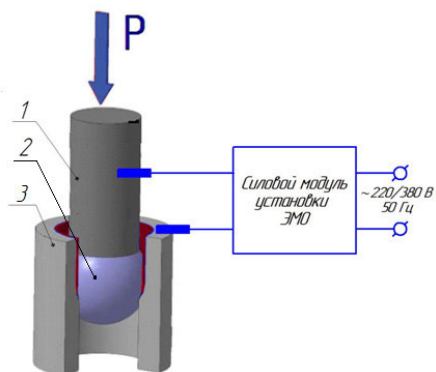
Схема электромеханического дорнования твердосплавным шаровым инструментом: 1 – толкатель; 2 – твердосплавный шар; 3 – деталь
